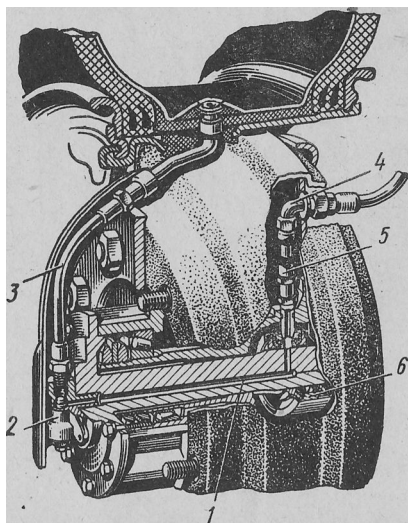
Схема подвода воздуха к шине колеса через полуось (см. рис. 53):
